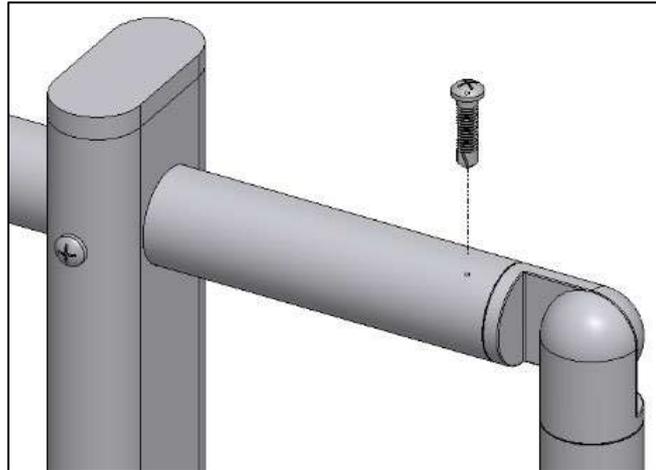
Fijación del terminal de cierre con tornillo autorroscante para conexión a los barandales.
